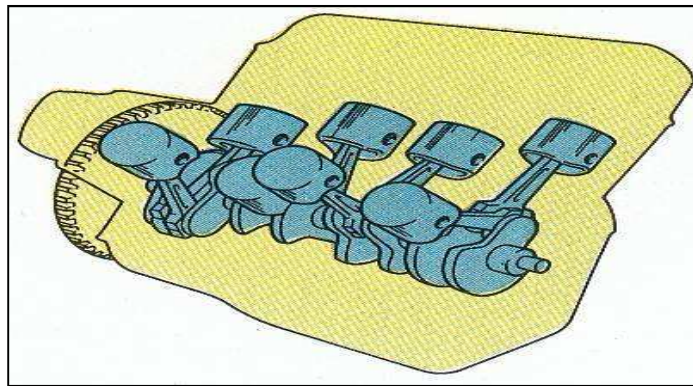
MOTOR EN V – 8 CILINDROS
